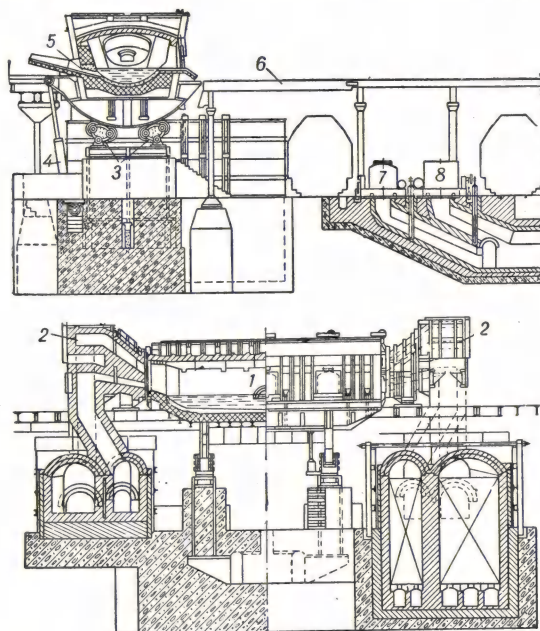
Схема устройства мартеновской печи (качающейся): 1 — рабочее пространство; 2 — головки; 3 — опорные ролики; 4 — поворотный механизм; 5 — выпускное отверстие; 6 — рабочая площадка; 7 — газовый перекидной клапан; 8 — воздушный перекидной клапан.
